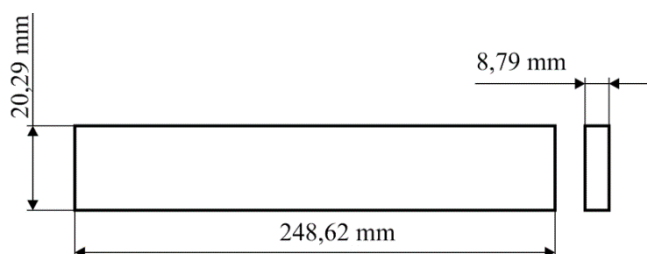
Dimensions principales de l'éprouvette en matériau composite.
